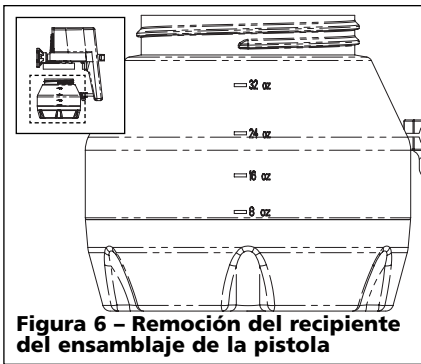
Remoción del recipiente del ensamblaje de la pistola
